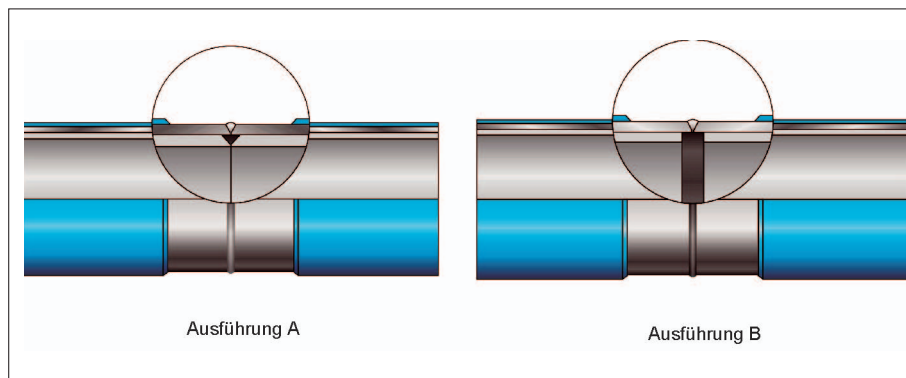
Stumpfschweißverbindungen nicht begehbare Rohrdimensionen
